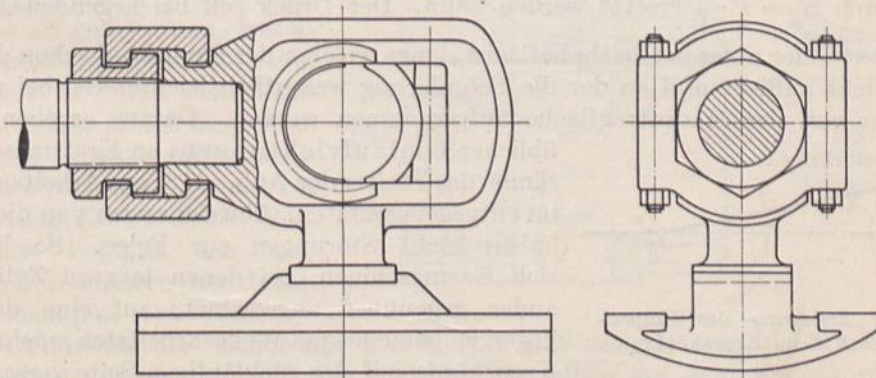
Gasmaschinenkreuzkopf von Ehrhardt und Sehmer, Saarbrücken.
